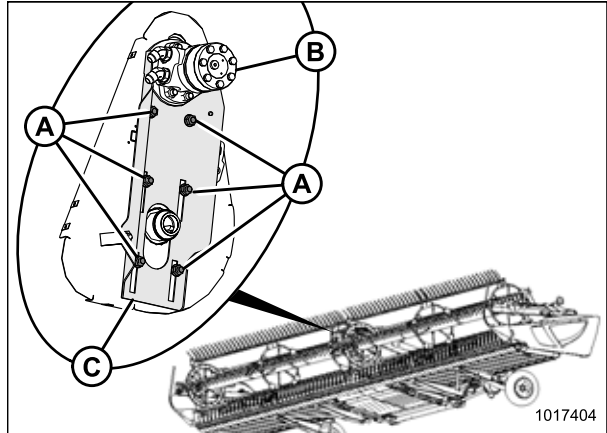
Haspelantrieb (Zeichnung ohne bestimmte Teile zwecks Übersichtlichkeit)
